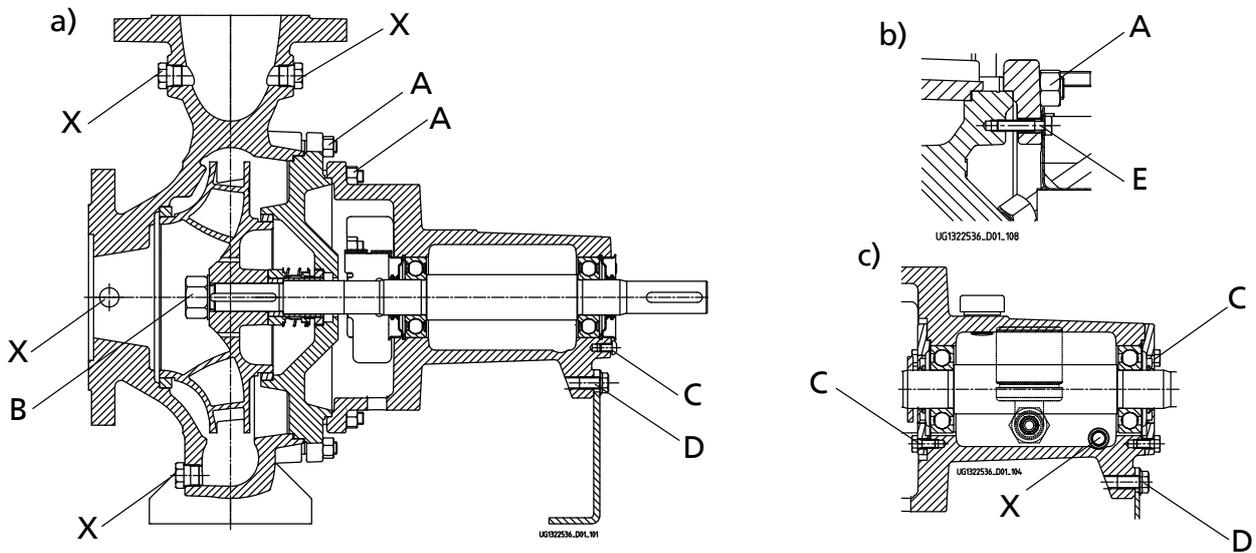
Места затяжки резьбовых соединений: исполнение с привинчиваемой крышкой корпуса и консистентной смазкой (а), исполнение с зажимной крышкой корпуса (b) и смазкой жидкой смазкой (с)
